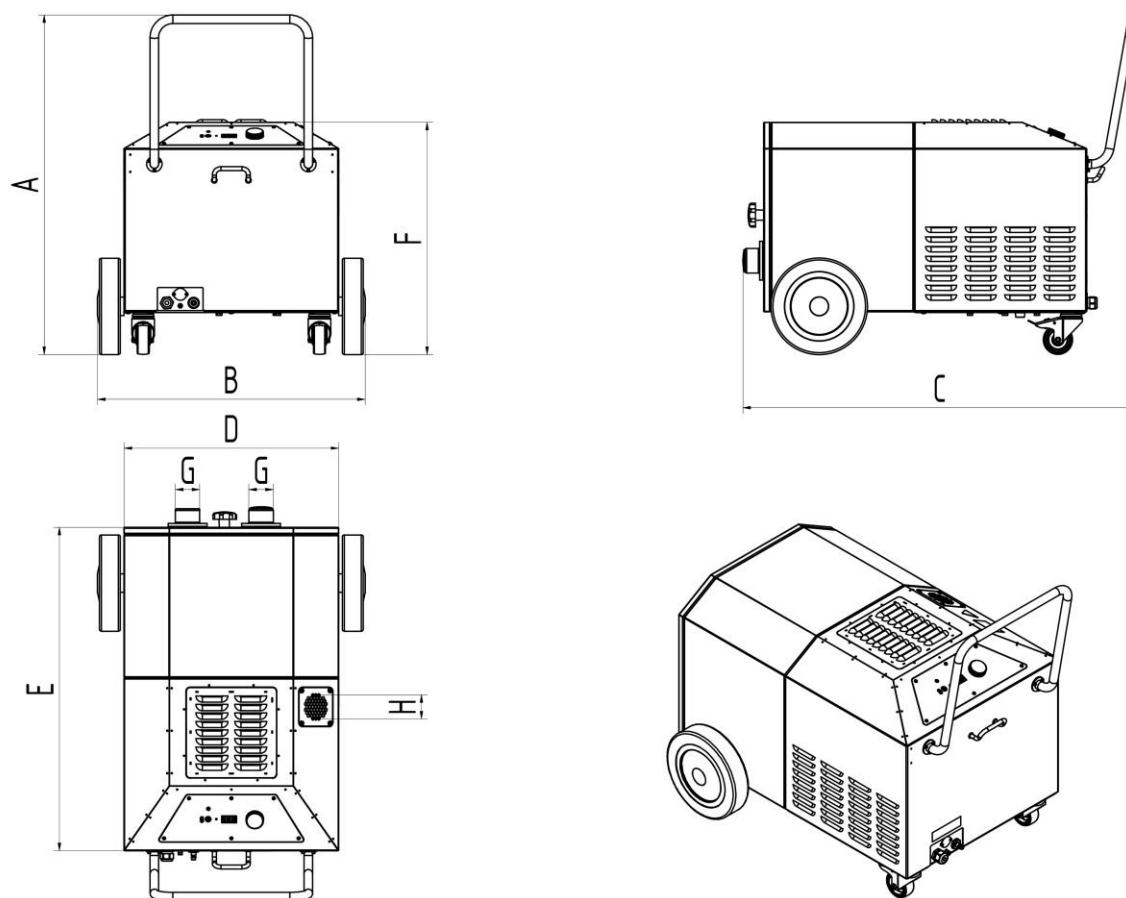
Габаритный чертеж – изделие без принадлежностей
